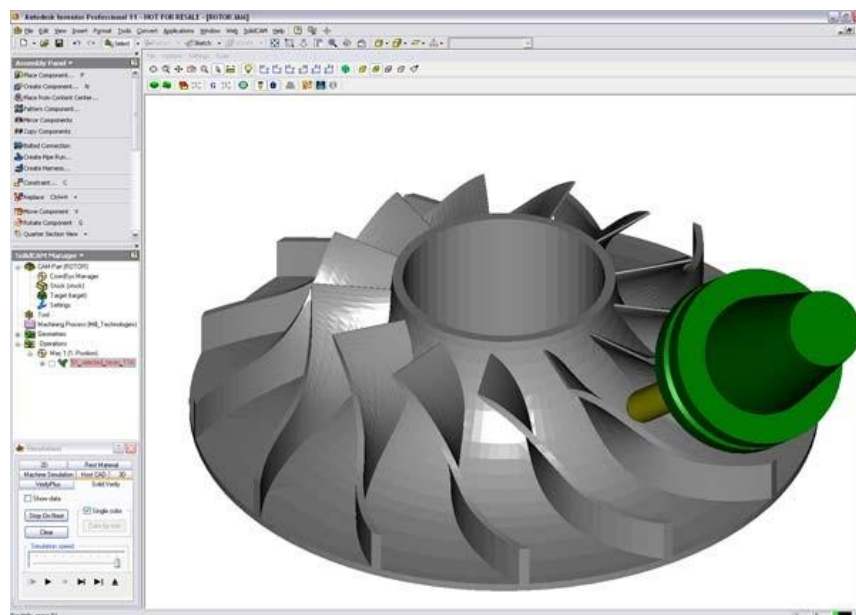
П'ятикоординатна фрезерна обробка складної криволінійної поверхні
